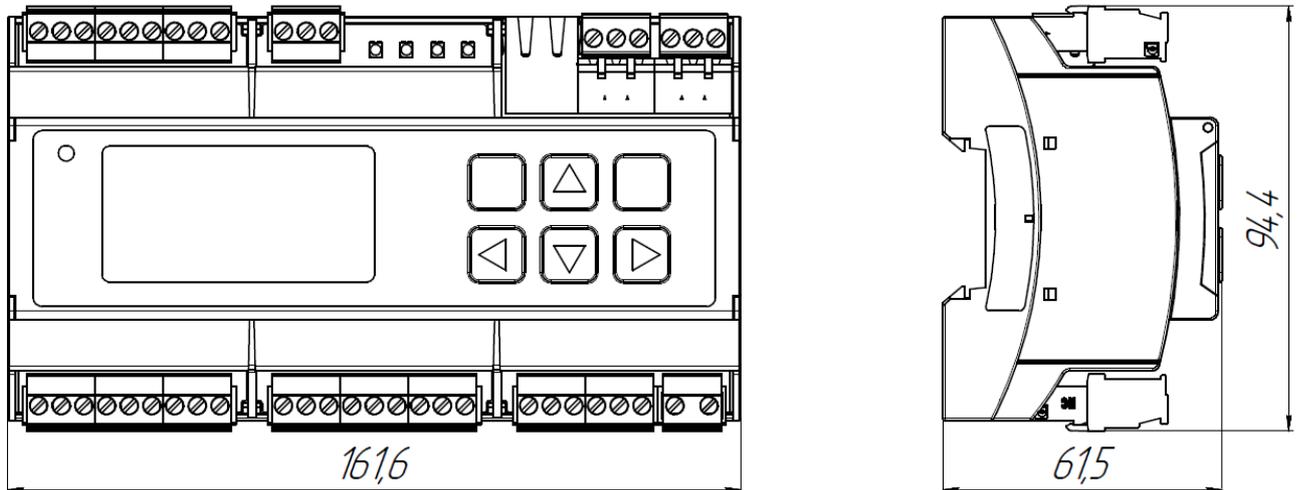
Габаритные и установочные размеры МАП-СГМ-110/Д.
